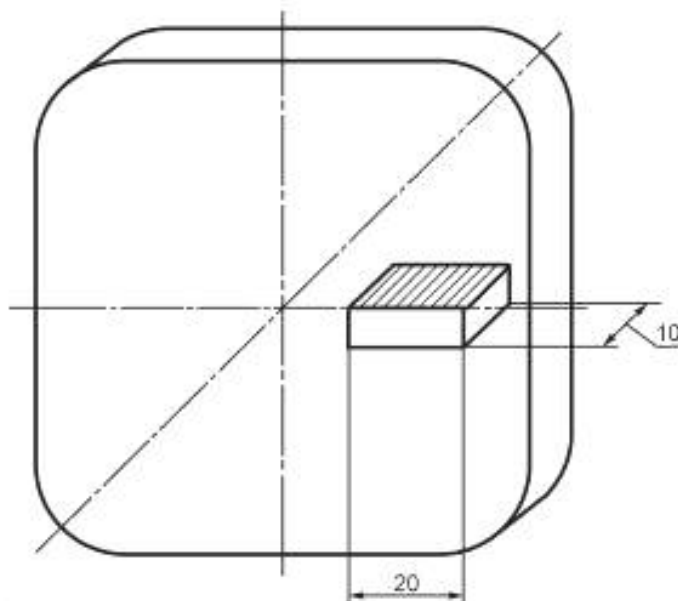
Образец от прутка или заготовки с диаметром или длиной стороны свыше 40 мм
